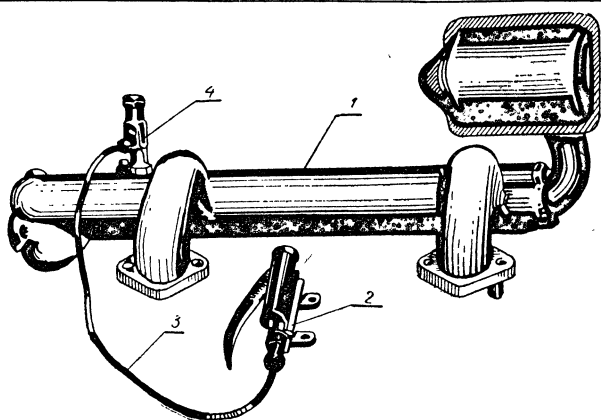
Приспособление для дозированного впрыска смеси во всасывающий коллектор:
